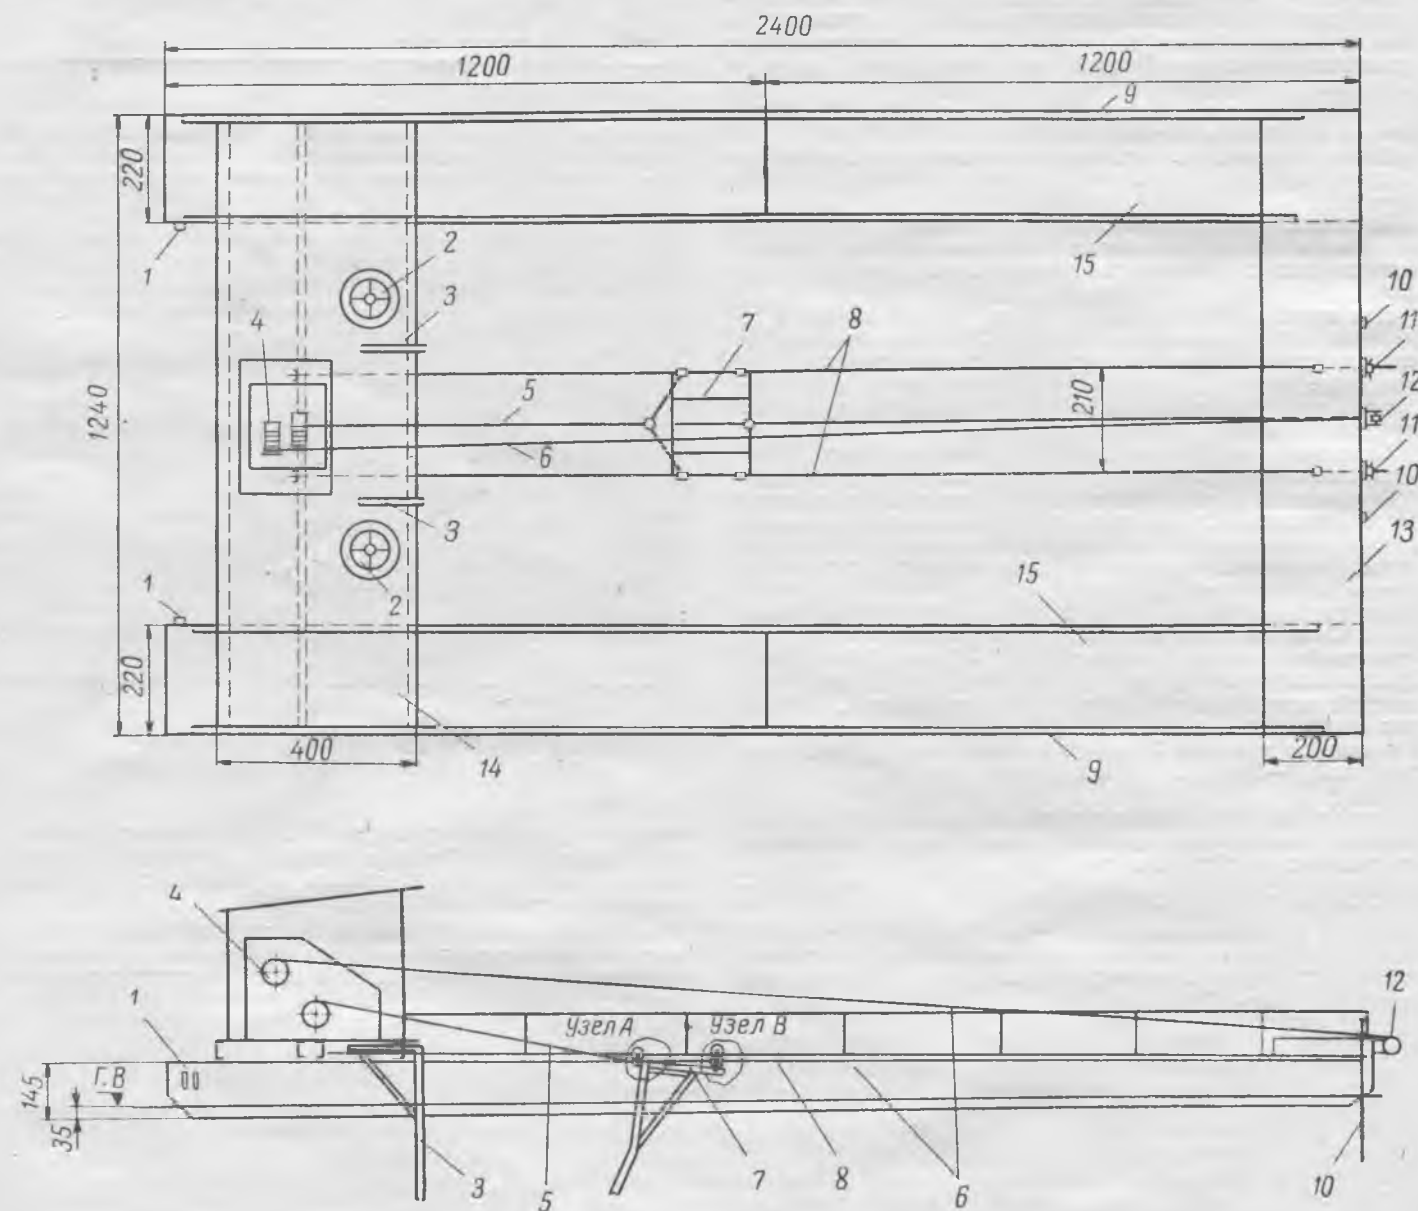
Схема модернизированного сплоточного комбинированного станка СКС:
